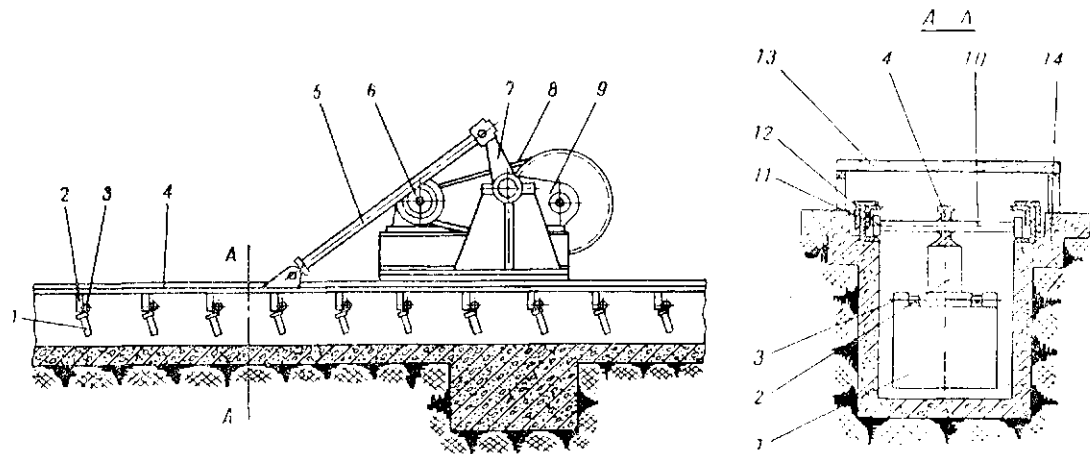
Схема штангового транспортера с горизонтальным расположением осей скребков:
